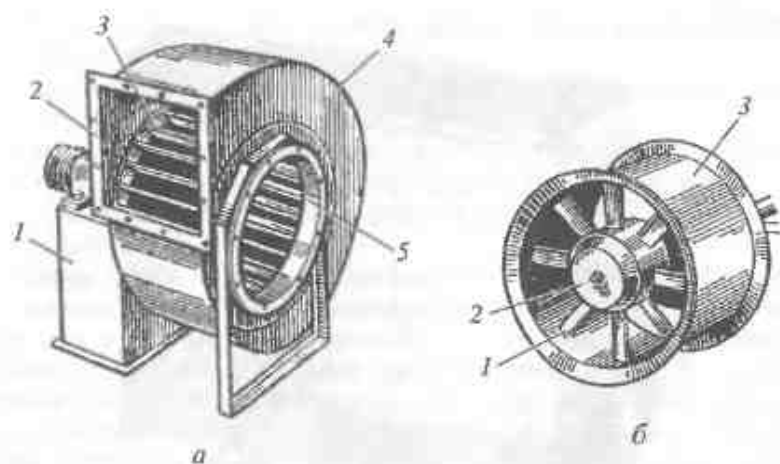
а — радиальный вентилятор (1 — станина; 2 — выхлопной патрубок; 3 — ротор; 4 — кожух; 5 — всасывающий патрубок); б — осевой вентилятор (1 — лопасти; 2 — ротор; 3 — кожух)
